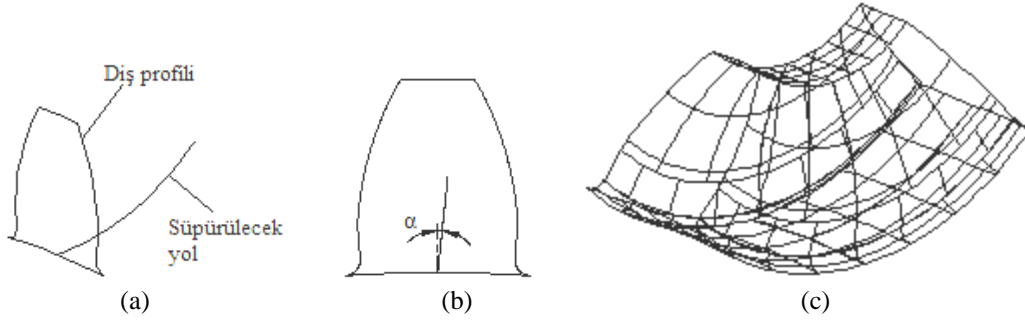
a) Diş profili ve yol b) sonsuz vida için helis açısı c) sonsuz vida için süpürülmüş bir diş modeli (a) a tooth profile and its path, b) helix angle for a worm gear c) a swept gear model for the worm gear)
